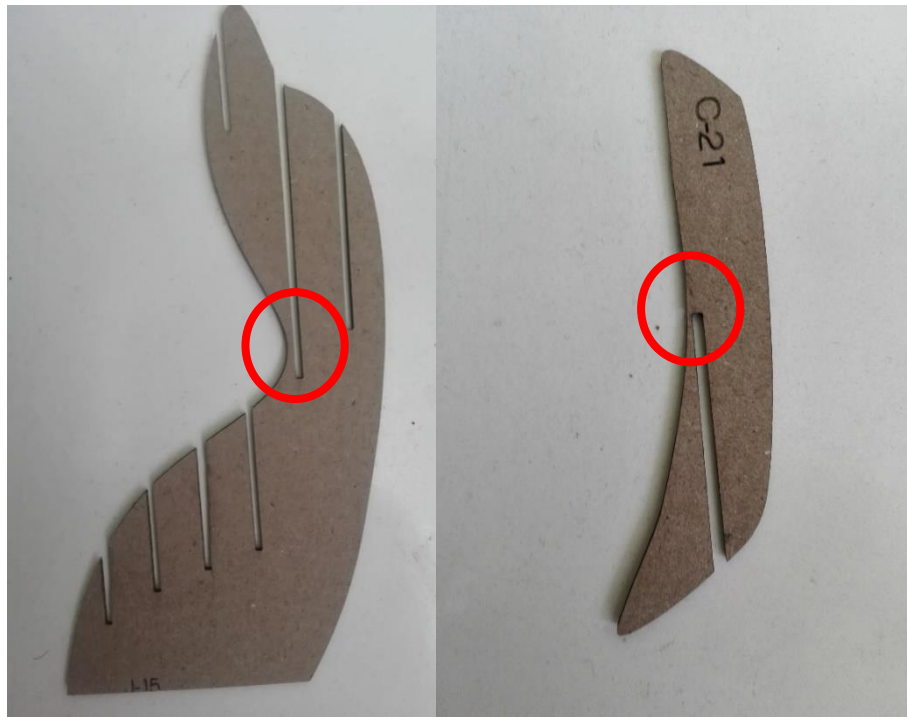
Proceso de ensamblado del prototipo en el Fab Lab de la Universidad Continental
